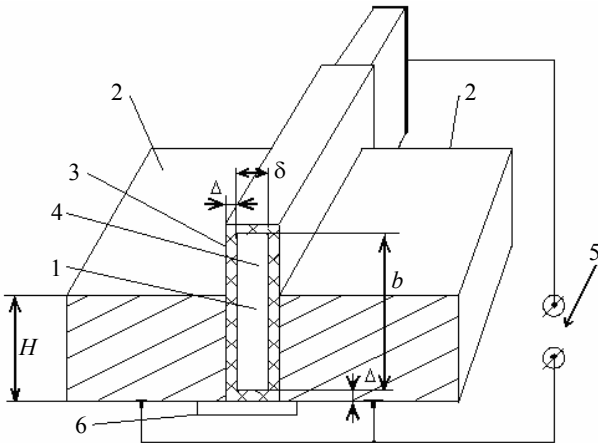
Сборка свариваемого стыка при ДС НПЭ:
